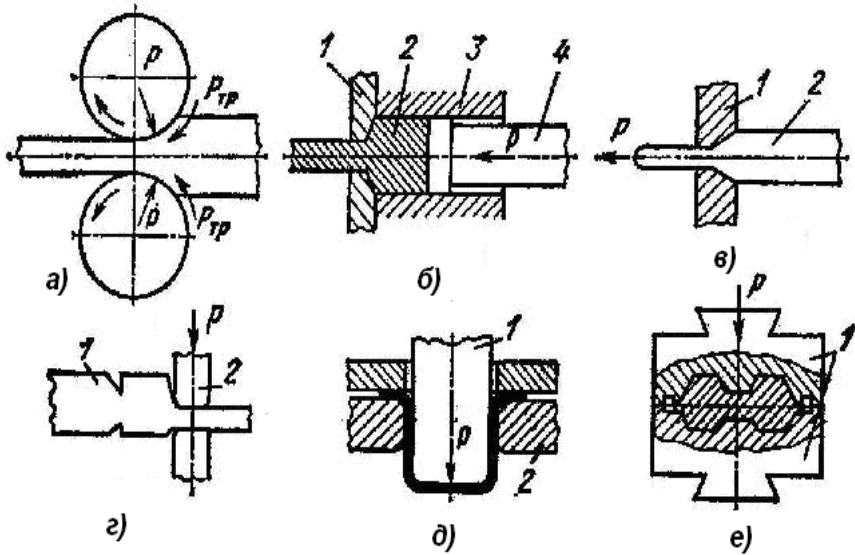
Схемы основных видов обработки металлов давлением: а) прокатки, б) прессования, в) волочения, г)ковки, д) одного из процессов листовой штамповки, е) одного из процессов объемной штамповки
